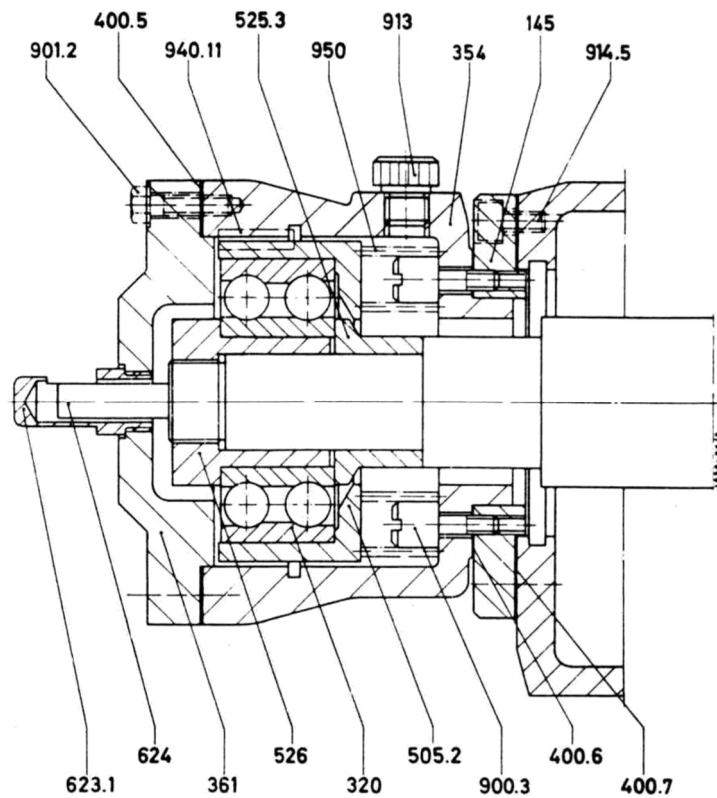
Dispositivo de compensación de empuje axial en ejecución con rodamientos antifricción para bombas con cojinetes de casquillo
